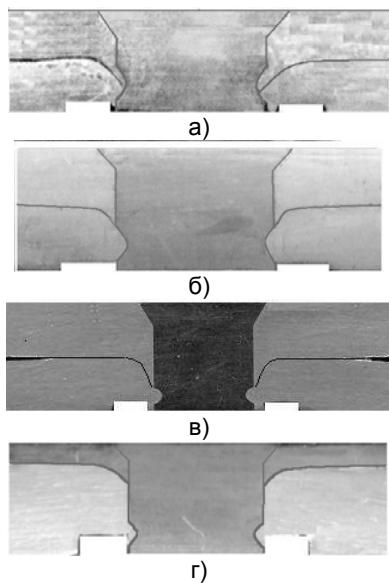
Виды соединений различных металлов недеформируемыми заклепками
